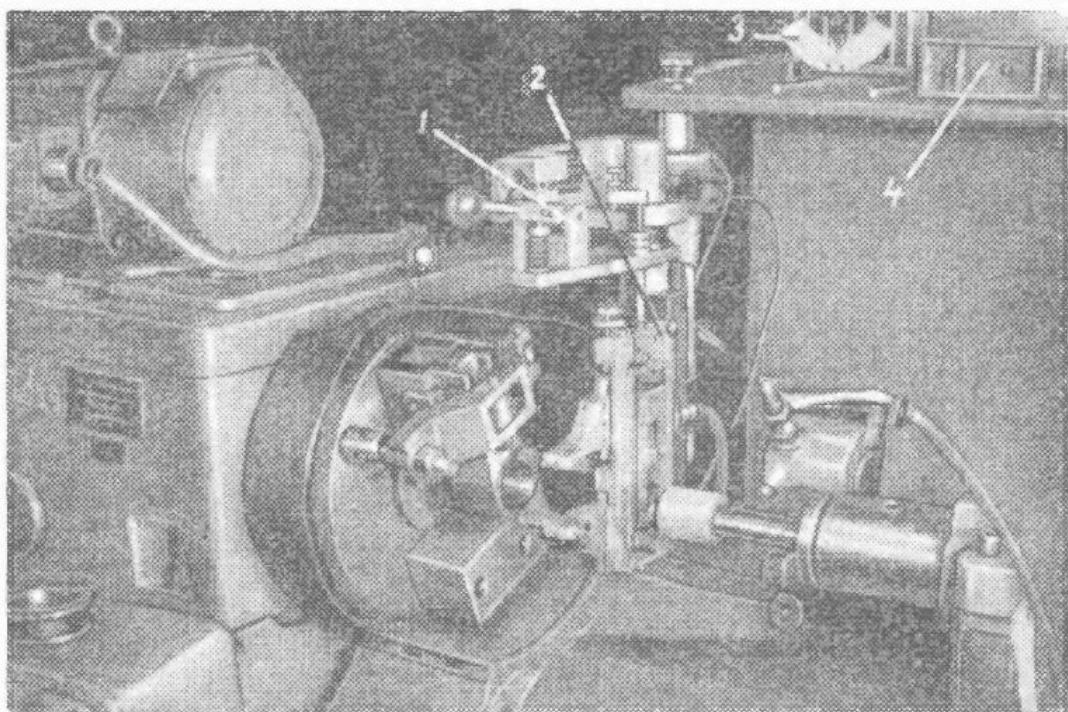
Пример установки устройства БВ-4025 на станке ЗА227
